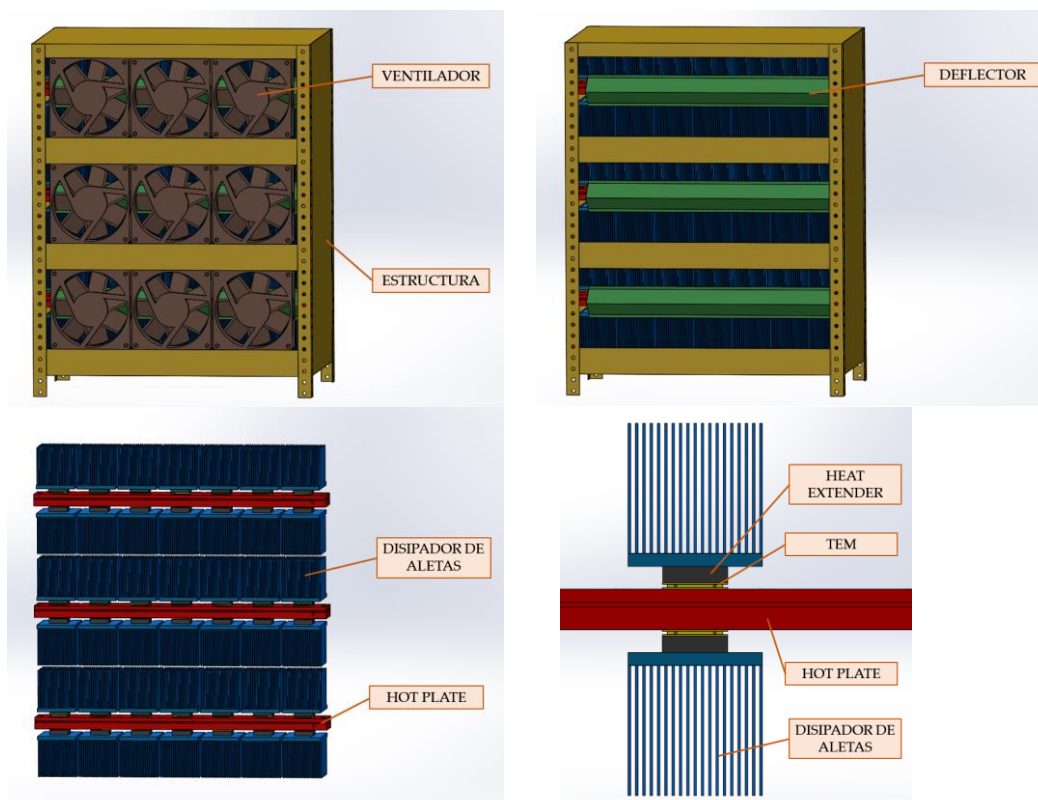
Componentes de la bomba de calor aire – agua (aeroterminia). Diseño en SOLIDWORKS.
